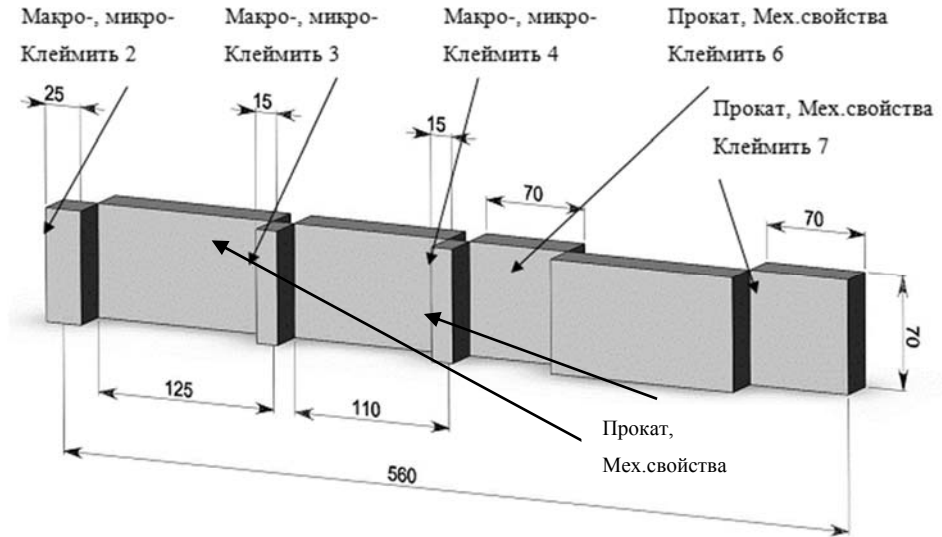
Схема раскроя на образцы заготовки №2
